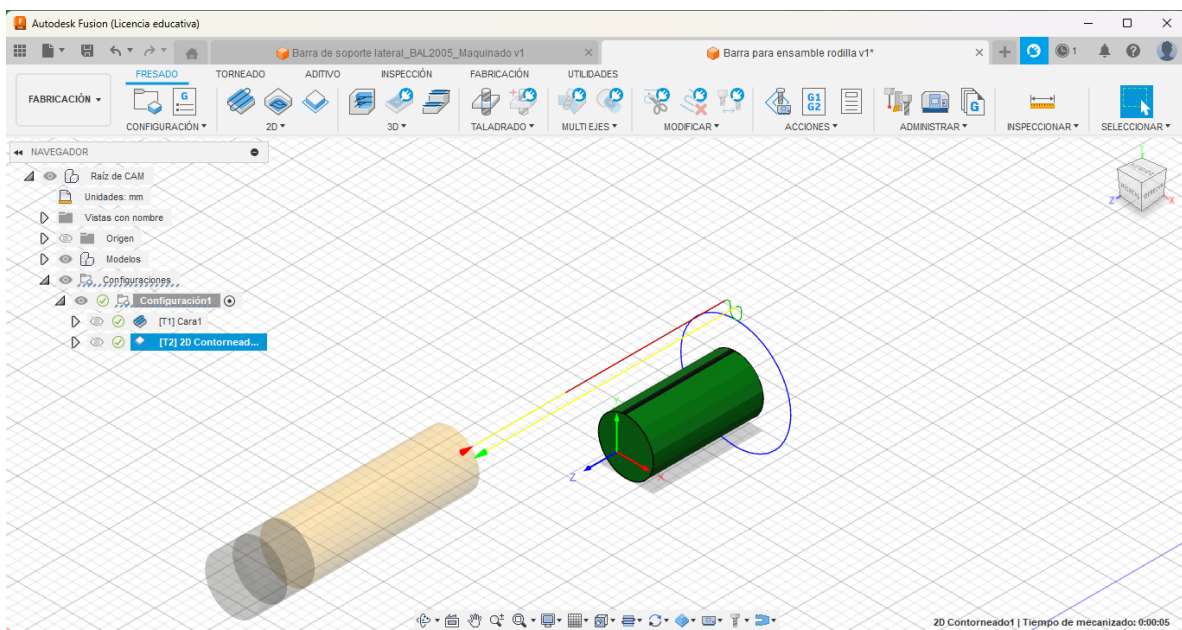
Maquinado de la pieza Barra de ensamble corta BAC2013
